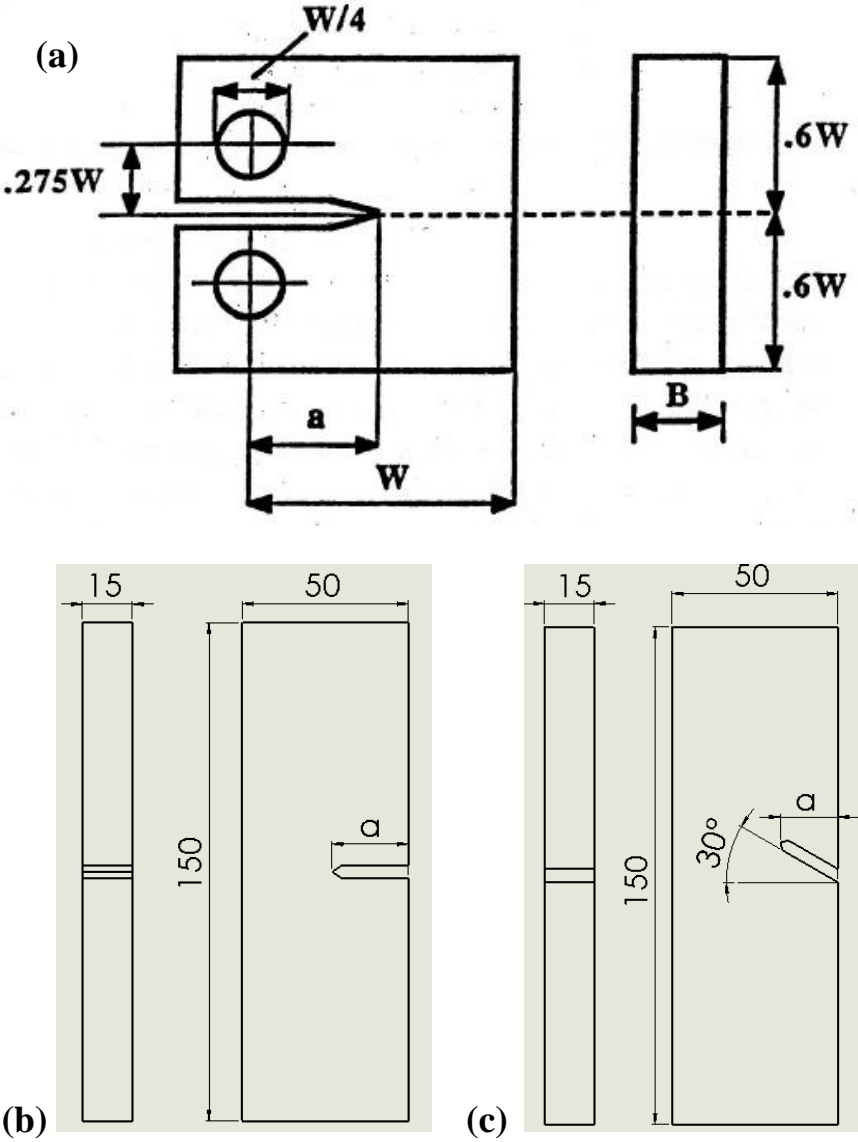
Géométries et dimensions des éprouvettes ; (a) CT, (b) SENT et (c) ASENT [2,3].
